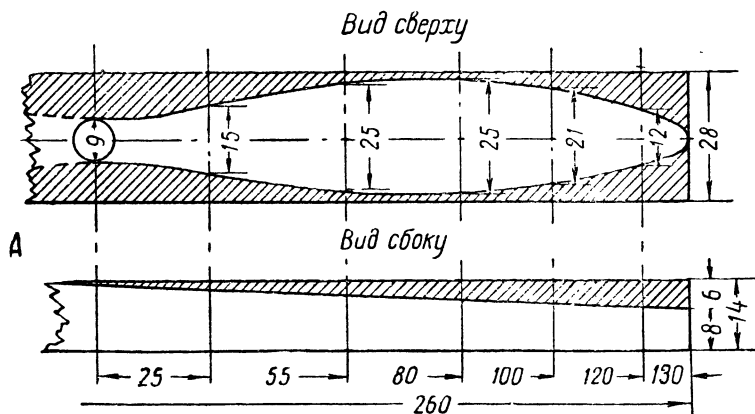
Винт: А) шаблоны винта (вид сбоку и вид сверху)
